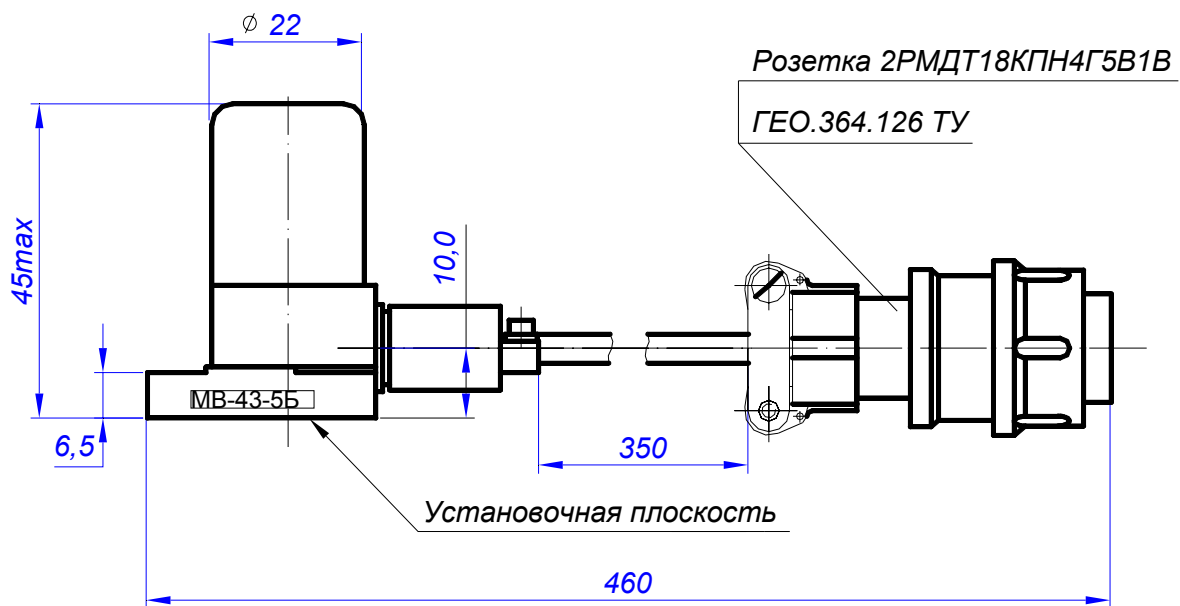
Габаритно-установочные размеры вибропреобразователя MB-43-5Б/0,35
